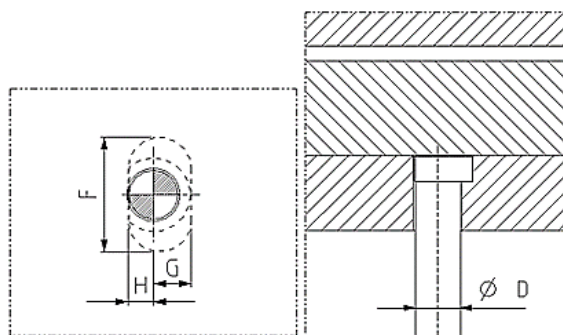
Extrator com posição (Grupo Simoldes, 2016)
